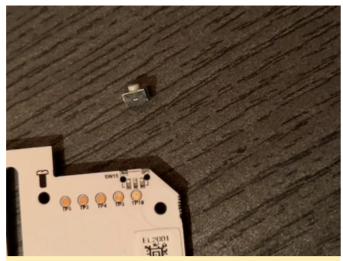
El componente SW15 también puede separarse de la placa durante el desmontaje
